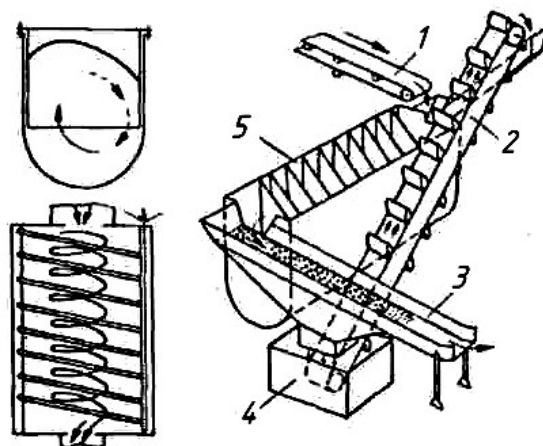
Схема механизации вибрационной очистки отливок: 1 – конвейер подачи отливок; 2 – элеватор возврата наполнителя; 3 – вибростол; 4 – бункер для наполнителя; 5 – контейнер с перегородками
